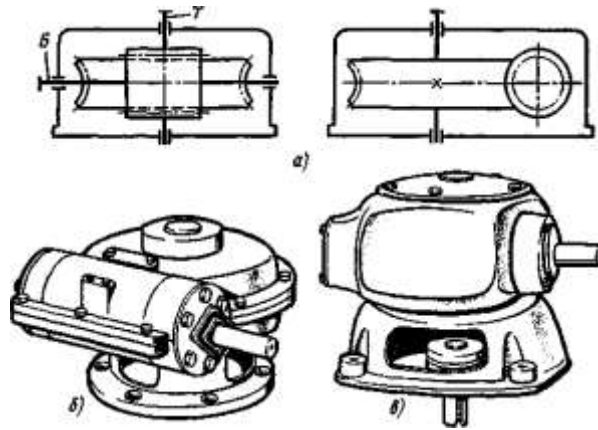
Червячный редуктор с вертикальным валом червячного колеса:
